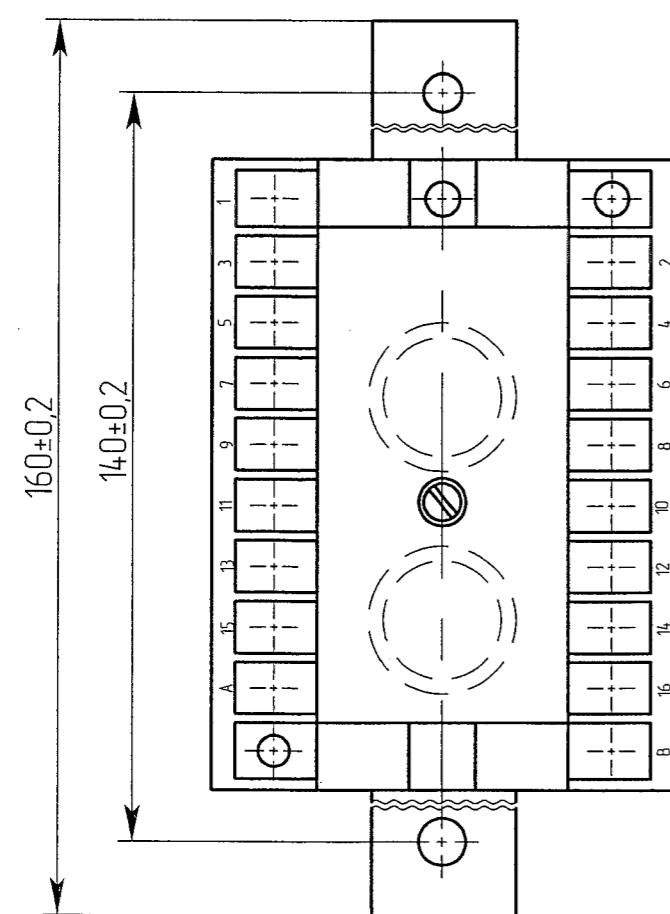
Реле типов PCB18-13-P-XXXX1, PCB18-23-P-XXXX1, PCB18-13-P-XXXX2, PCB18-23-P-XXXX2. Остальное см. рисунок Б.2
